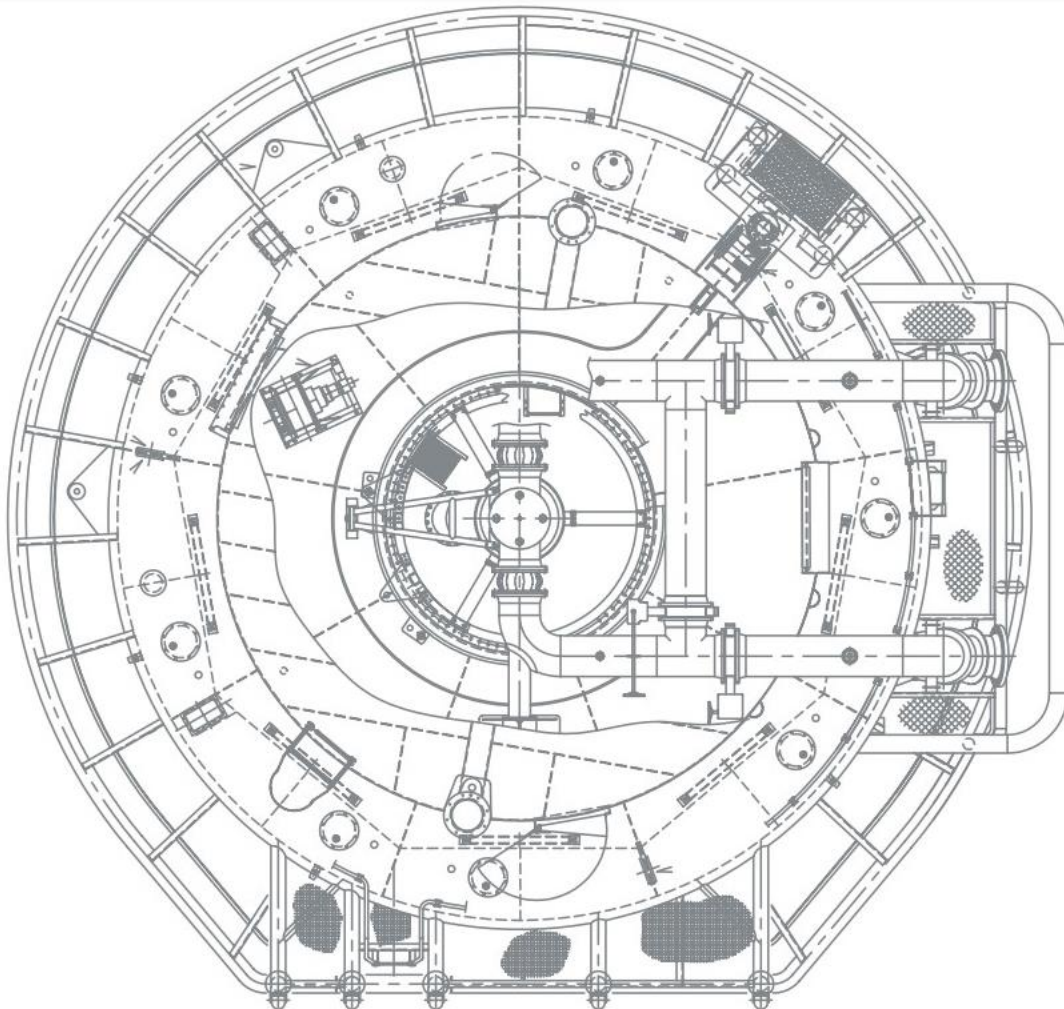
Vista en planta de la monoboya bajo estudio.[14]
